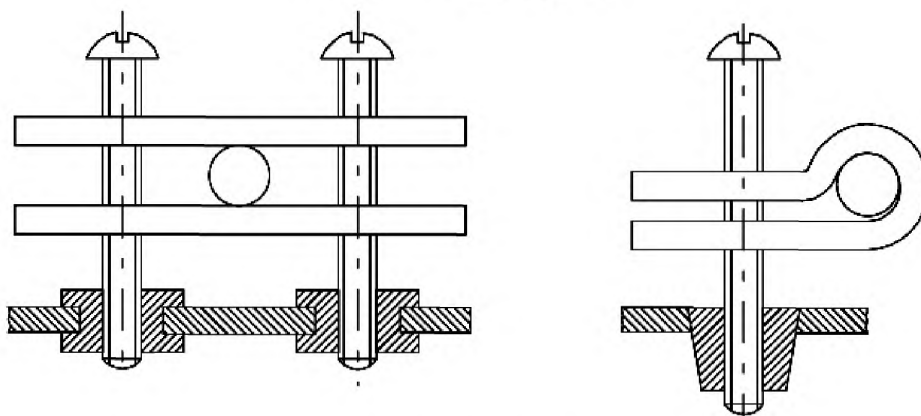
Приспособление для испытания вдавливанием шарика
